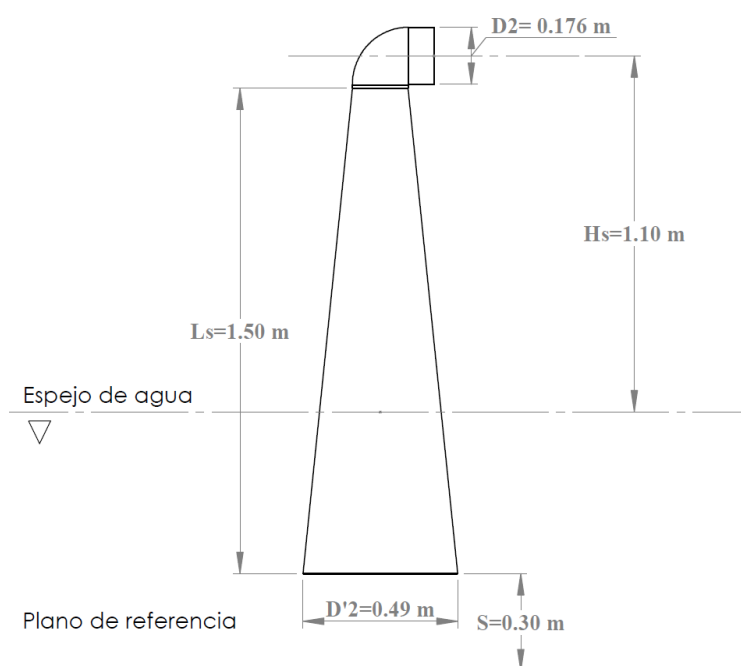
Dimensiones principales del banco de pruebas.
